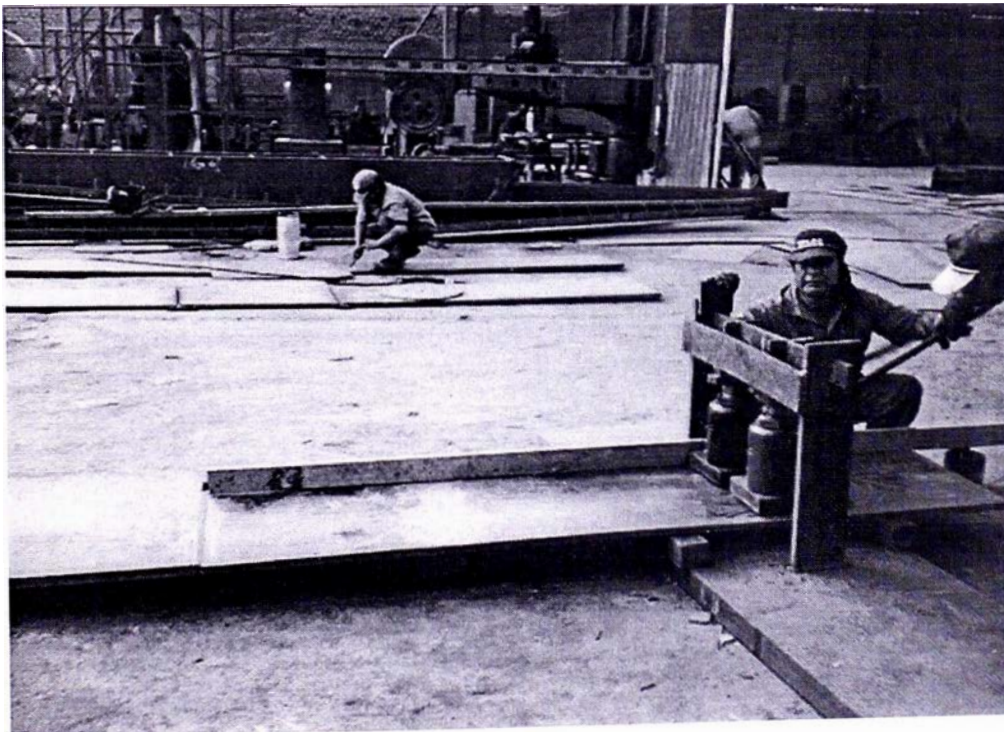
Enderezado de Planchas de Acero en Frío
